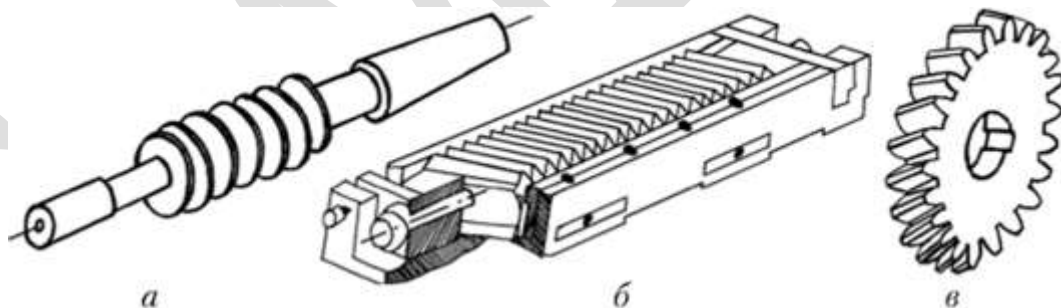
Типи шеверов: *а* — черв'ячний; *б* — рейковий; *в* — дисковий [5]
